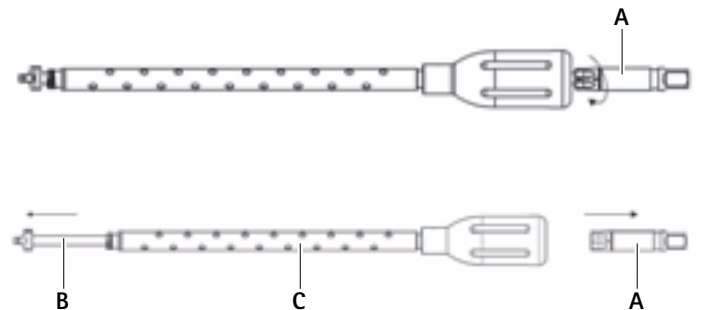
Demontage des TH-Schraubendrehers mit Gewinde
